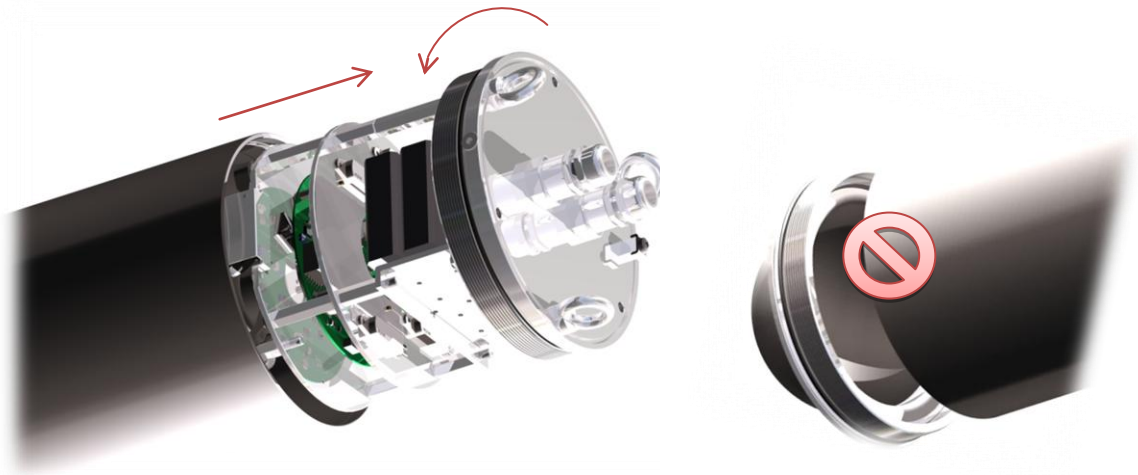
Öffnen des Deckelflansches Typ T08-TNXCD
